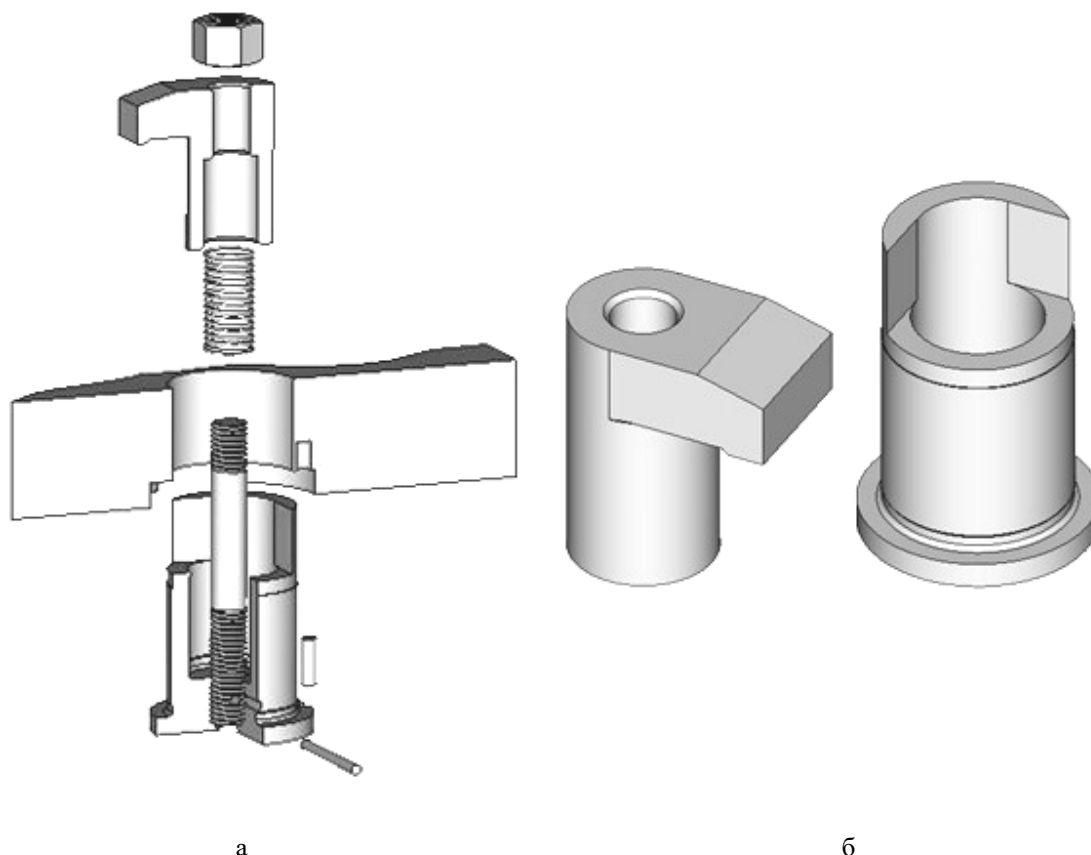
Детали зажимного устройства с Г-образным прихватом:
